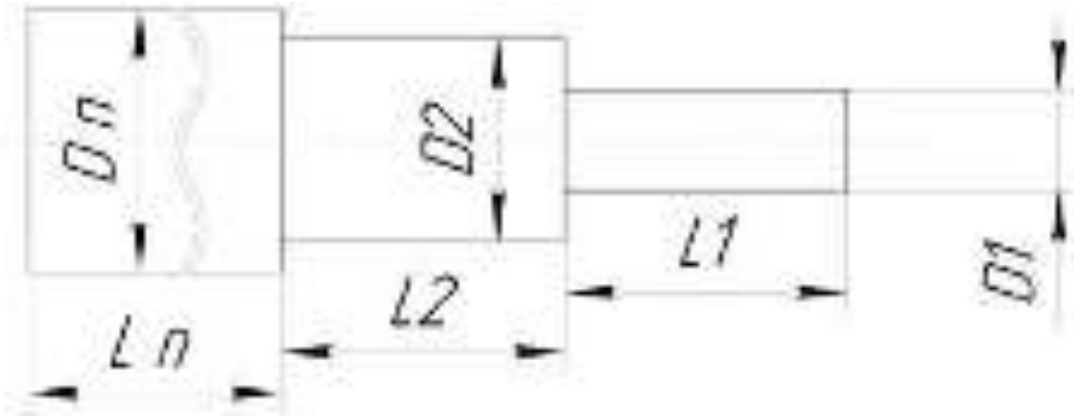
загальна схема корпусу осьового інструменту з СНП
